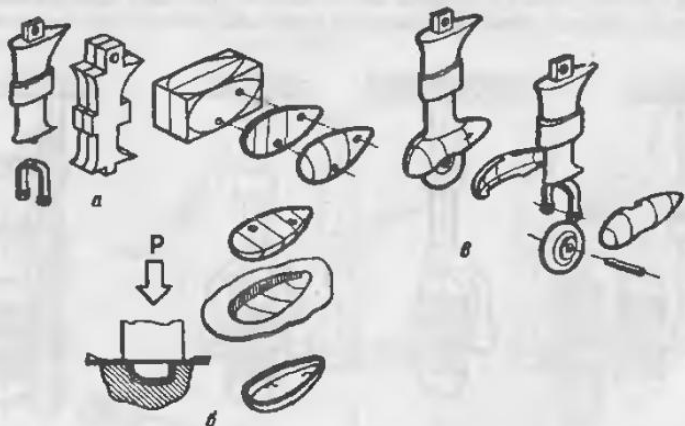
Образец изготовления стойки шасси с обтекателями на колесах (самолет Фоккер D-21): а - изготовление стойки; б - изготовление пуансона для штамповки в свинец половинок обтекателя; в - сборка (пайка) стойки
